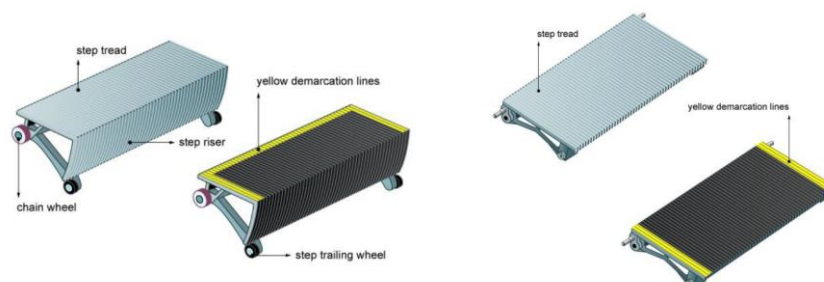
Peldaños (Izquierda) y paletas (Derecha).
